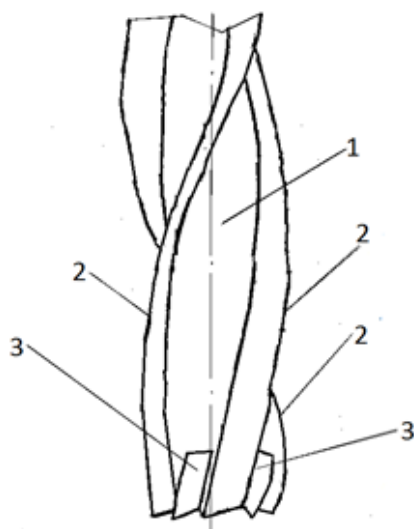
Длиннокромочная концевая фреза с дополнительно установленными зубьями в торцовой части: 1 – корпус фрезы; 2 – зубья основной части фрезы; 3 – дополнительно установленные специальные зубья в торцовой части
